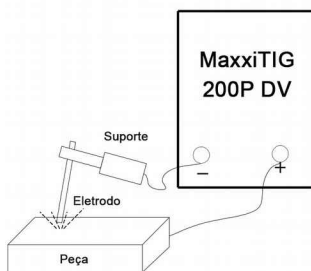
Conexão negativa para soldagem com eletrodo revestido
